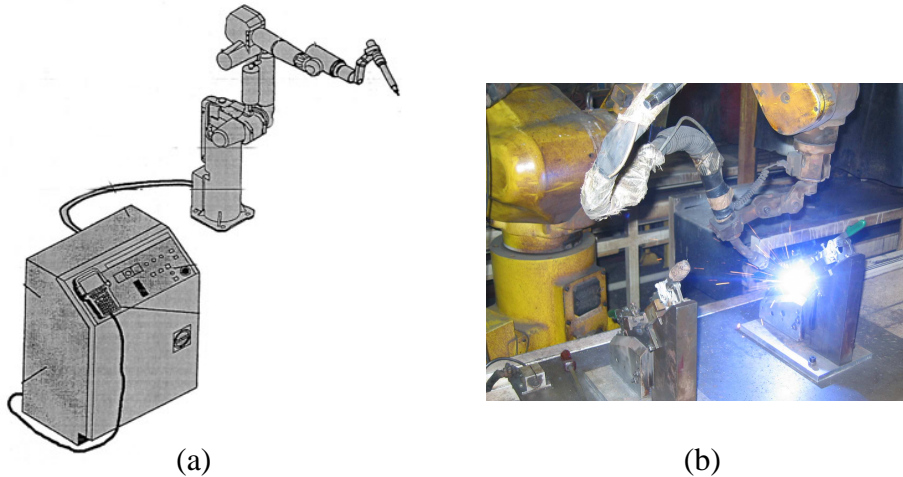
(a) le système de soudure surveillé avec son système de contrôle. (b) Soudure de deux pièces métalliques.
